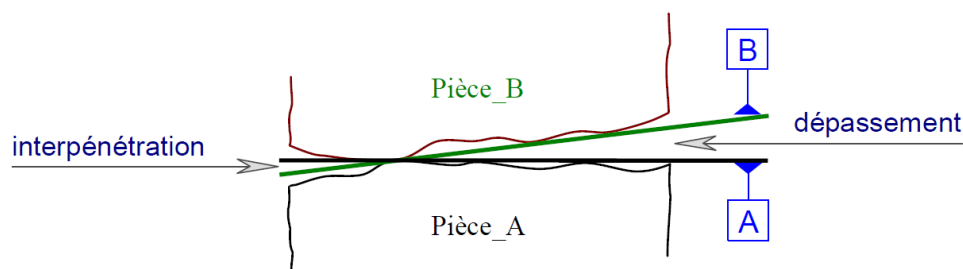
Contact plan/plan (Radouani, 2003)
